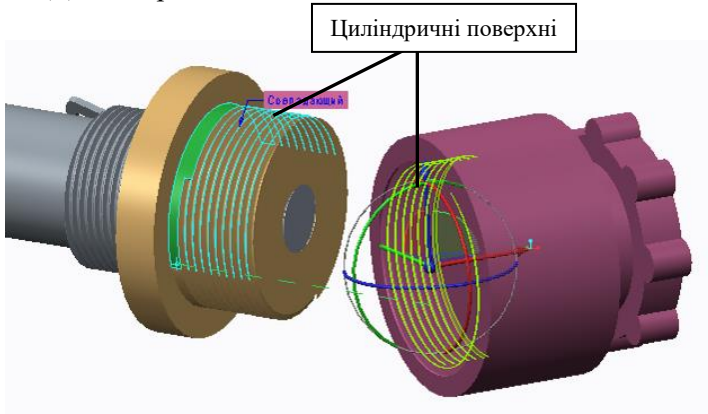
Виділення циліндричних поверхонь деталей
